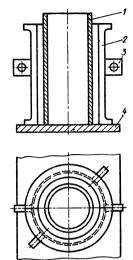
Приспособление для вертикальной заливки баббитом вкладышей:
